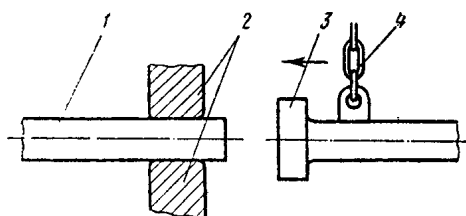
Схема высадки нагретого конца длинной заготовки («романение»): 1 — заготовка, 2 — бойки, 3 — штанга («роман»), 4 — цепь
